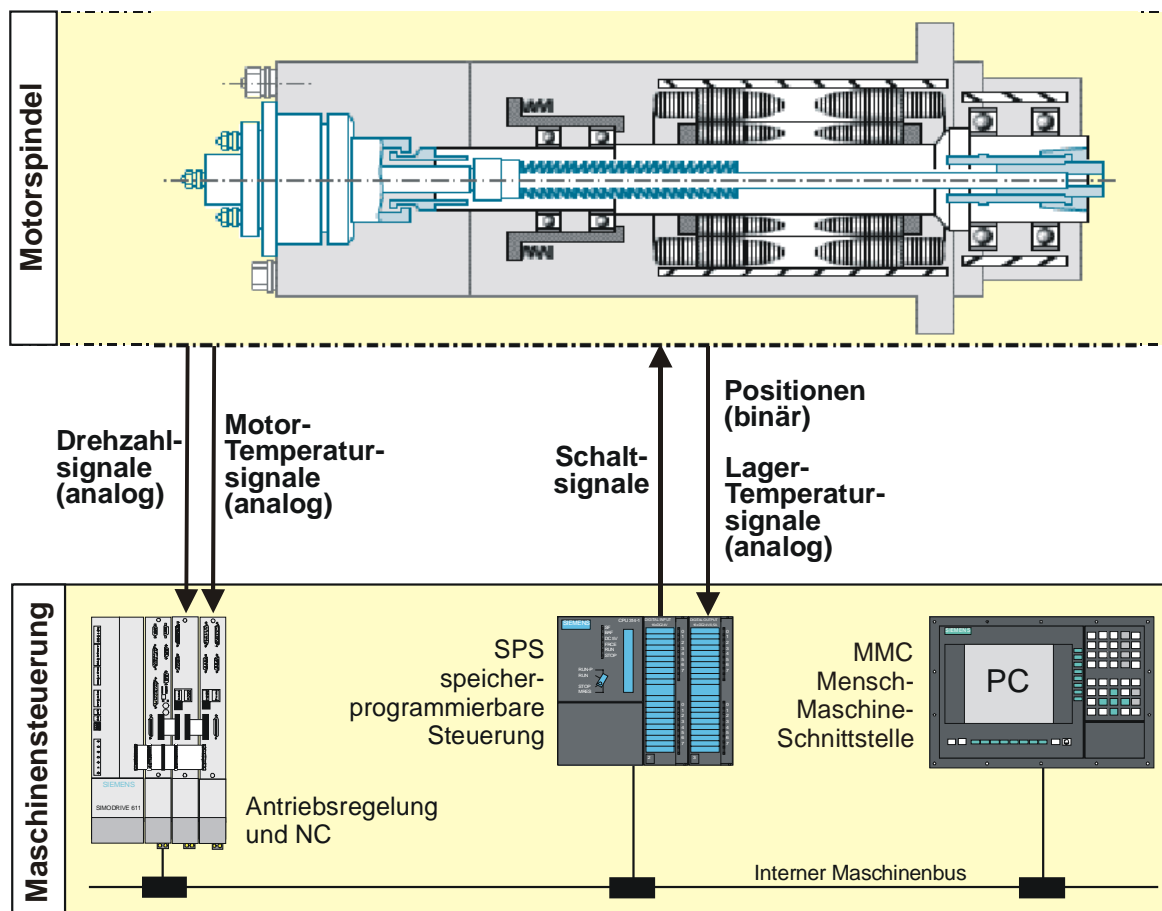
Zusammenspiel der Maschinensteuerung mit einer Motorspindel
